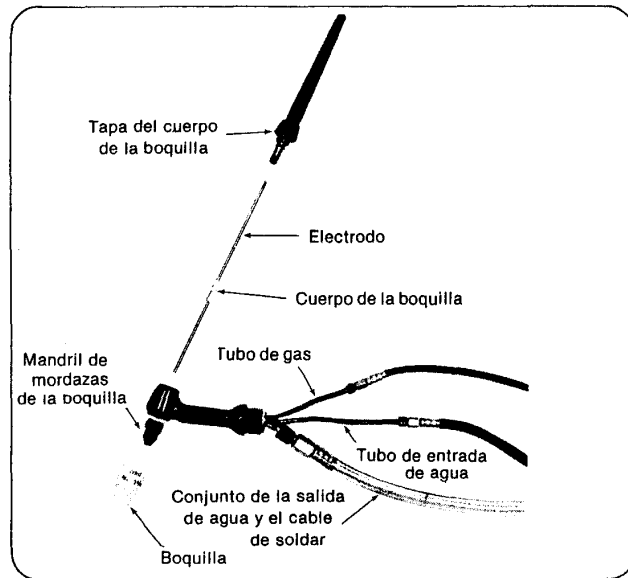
Vista esquemática de un conjunto de soplete y cable enfriado por agua para soldadura TIG.
